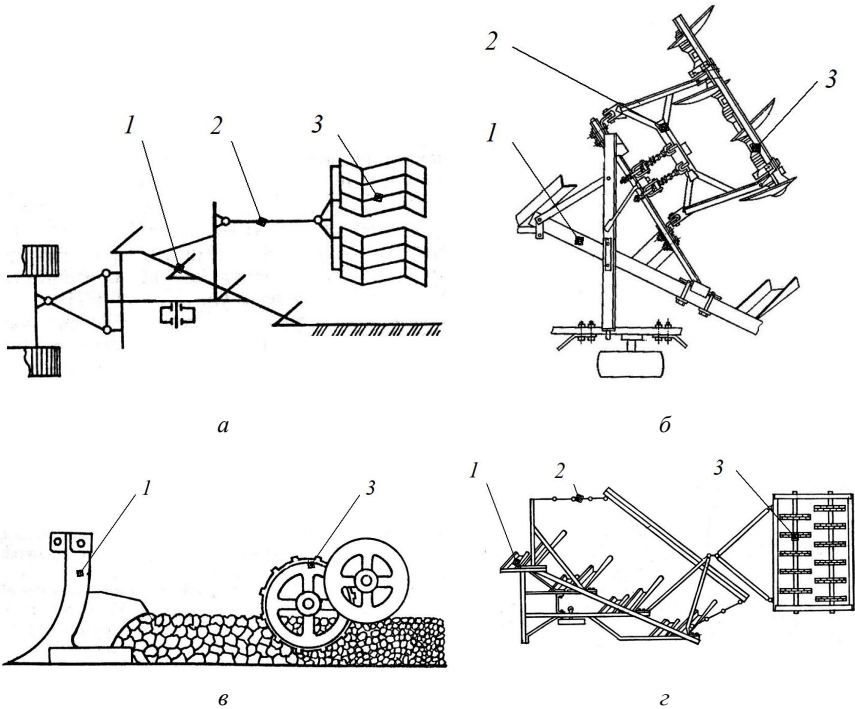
Схемы приспособлений для поверхностной обработки почвенного пласта в конструкциях пахотных агрегатов с использованием:
